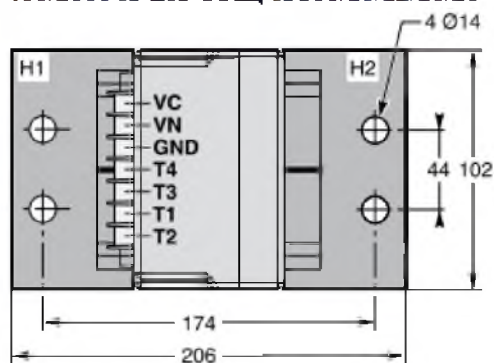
Габаритные и установочные размеры блока задержки срабатывания для расцепителя MN
